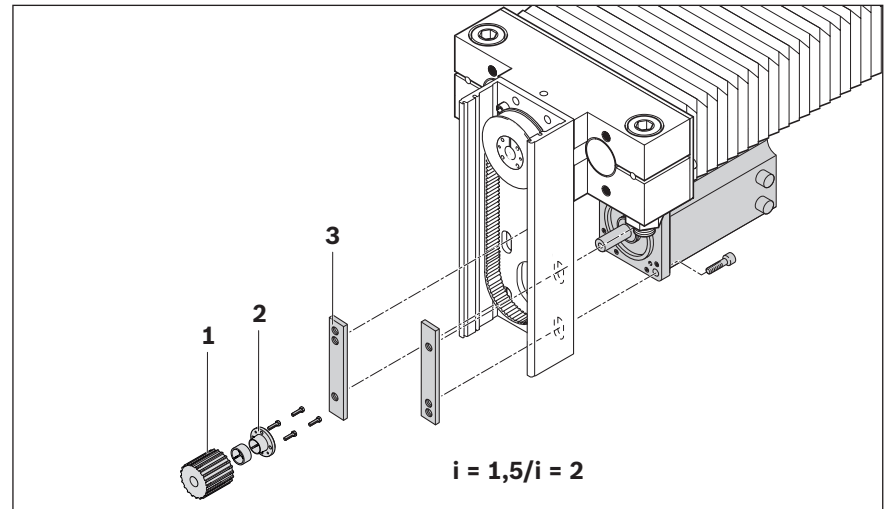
Motor und motorseitiges Riemenrad montieren ($i = 1,5/2$)
